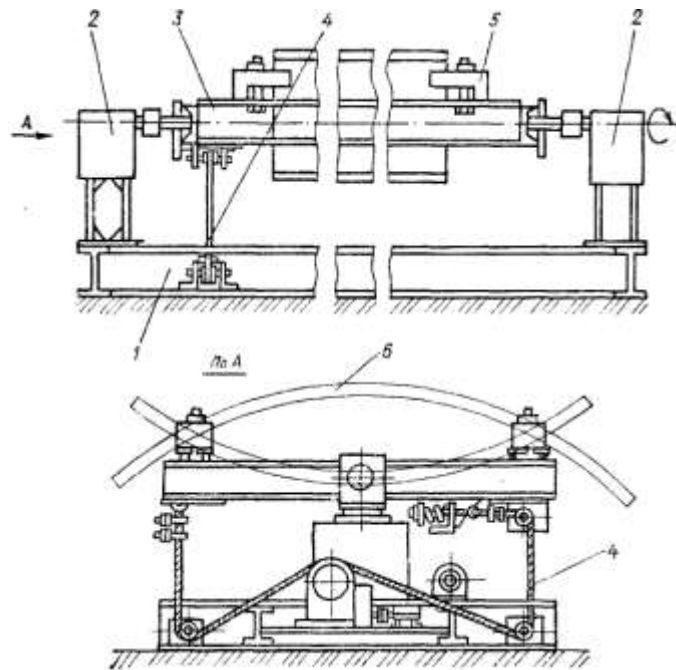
Вращатель для сварки на монтажной площадке укрупненных блоков кожуха доменной печи
